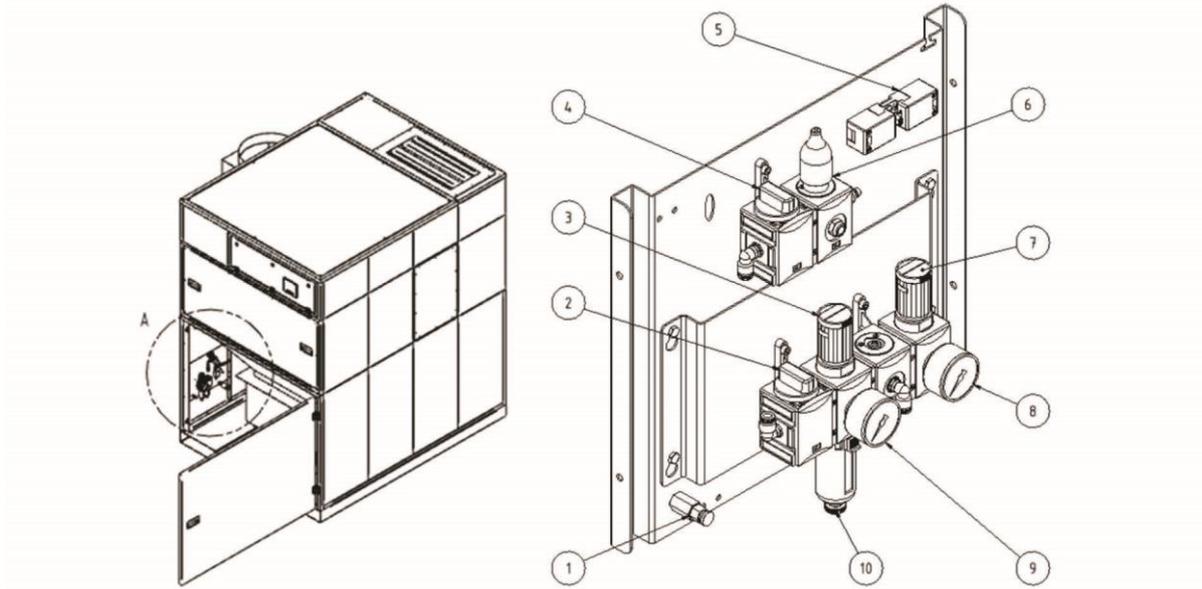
Montaje de la caja de conexiones del lado de aspiración
